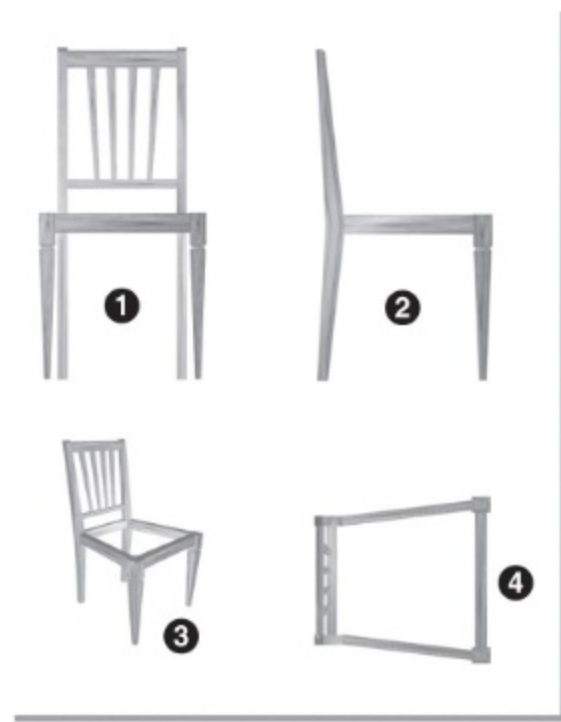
Detalle del dibujo realizado a tamaño natural sobre cartulina con las vistas principales: 1. alzado; 2. perfil; 3. perspectiva; 4. planta
